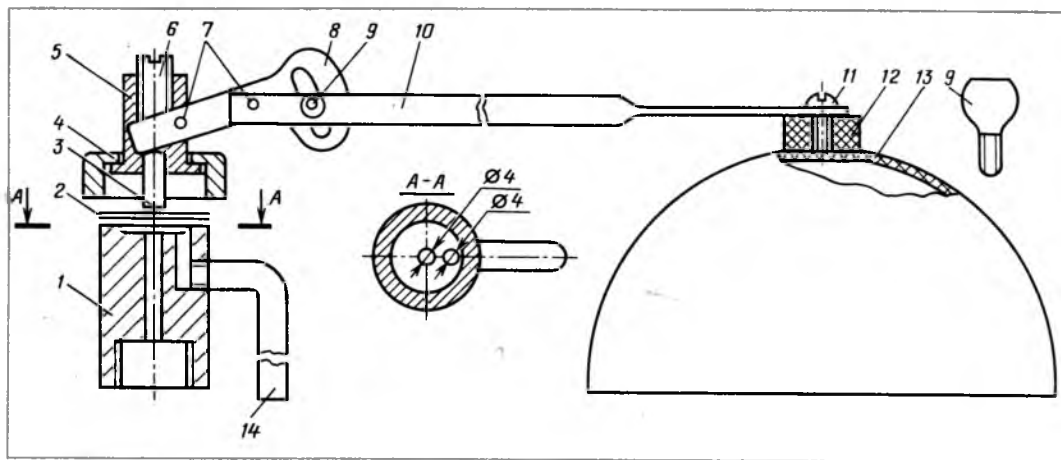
Вертикальный поплавковый клапан: 1 — корпус; 2 — резиновая прокладка; 3 — шток; 4 — накидная гайка; 5 — валик; 6 — винт; 7 — шпильки; 8 — рычаг фасонный; 9 — баранек; 10 — рычаг поплавка; 11 — винт; 12 — гайка пластмассовая; 13 — поплавок; 14 — рубка сливная
